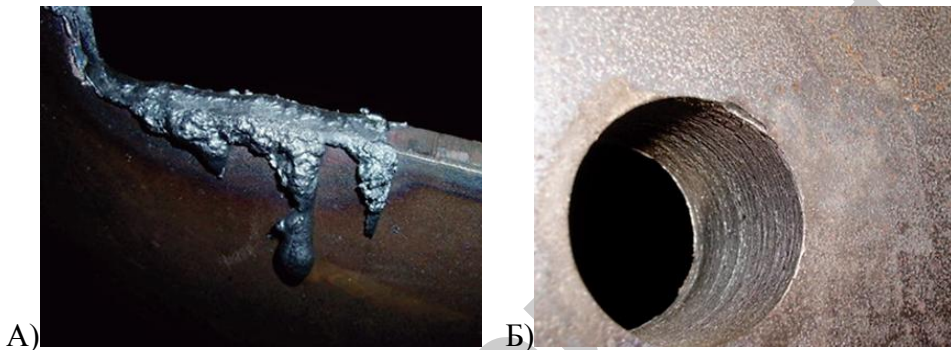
А – Грот, окалина, капли металла от газовой резки, 5Б – Острые кромки отверстий после сверления
